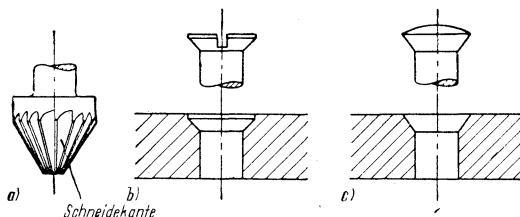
Zum Versenken benutzt man den Spitzsenker (a); richtige Senkung für Senkschraube (b) und für Senkniet (c)
